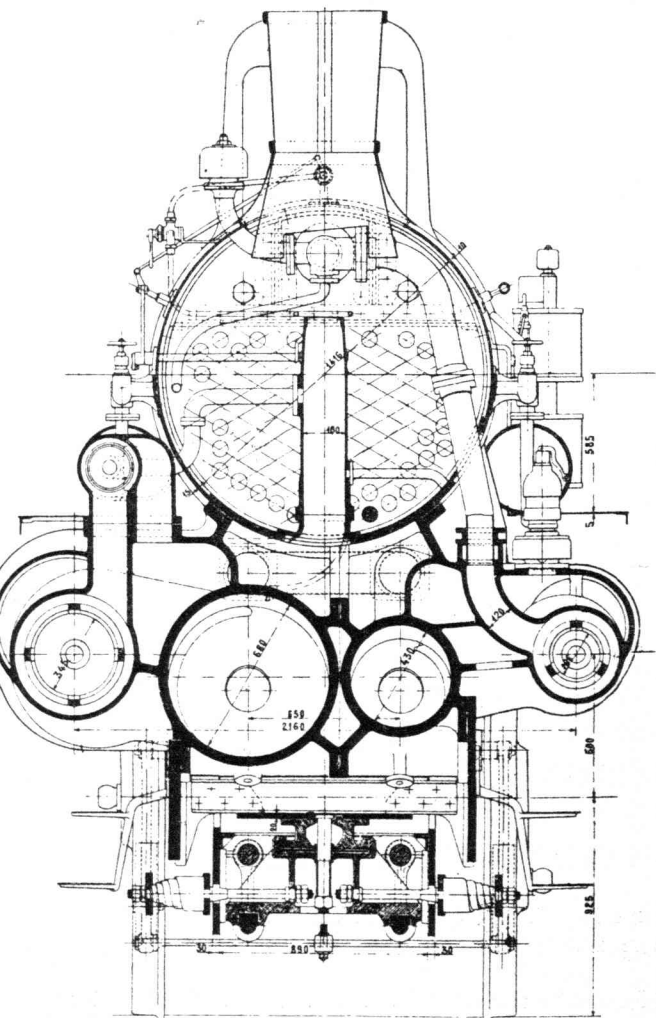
Querschnitt durch Zylinder und Rauchkammer der Serie 630 F. S. J.
